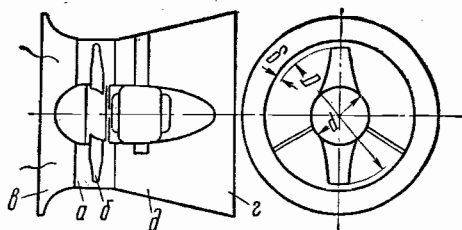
Схема осевого вентилятора: а — цилиндрический кожух; б — лопаточное колесо; в — входное отверстие; г — выпускное отверстие; д — диффузор
